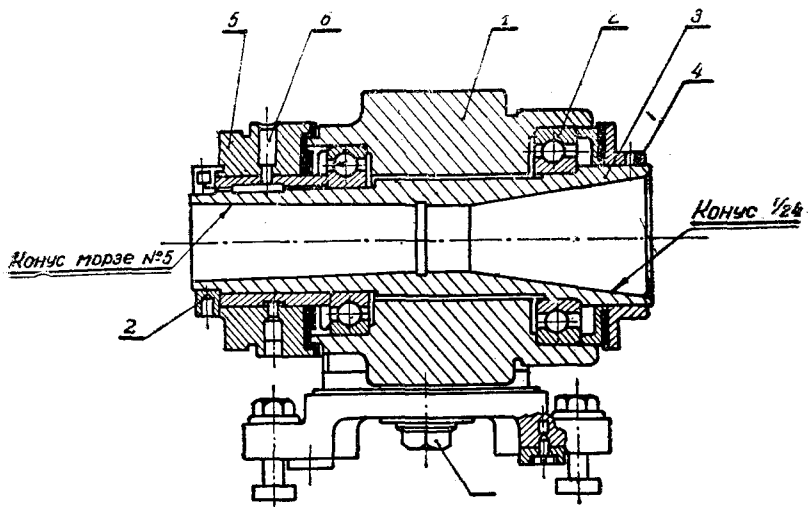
Разрез по оси шпинделя универсально-заточной головки
